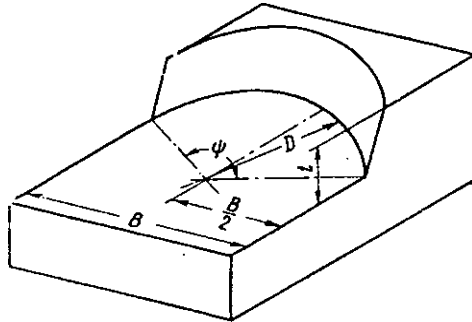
Заготовка у процесі обробки торцевою фрезою
